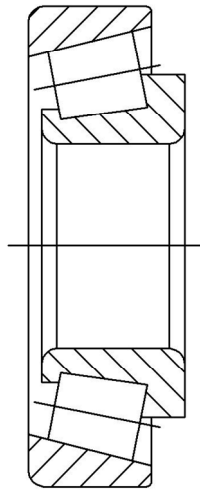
Роликовий підшипник радіально-упорний конічний
